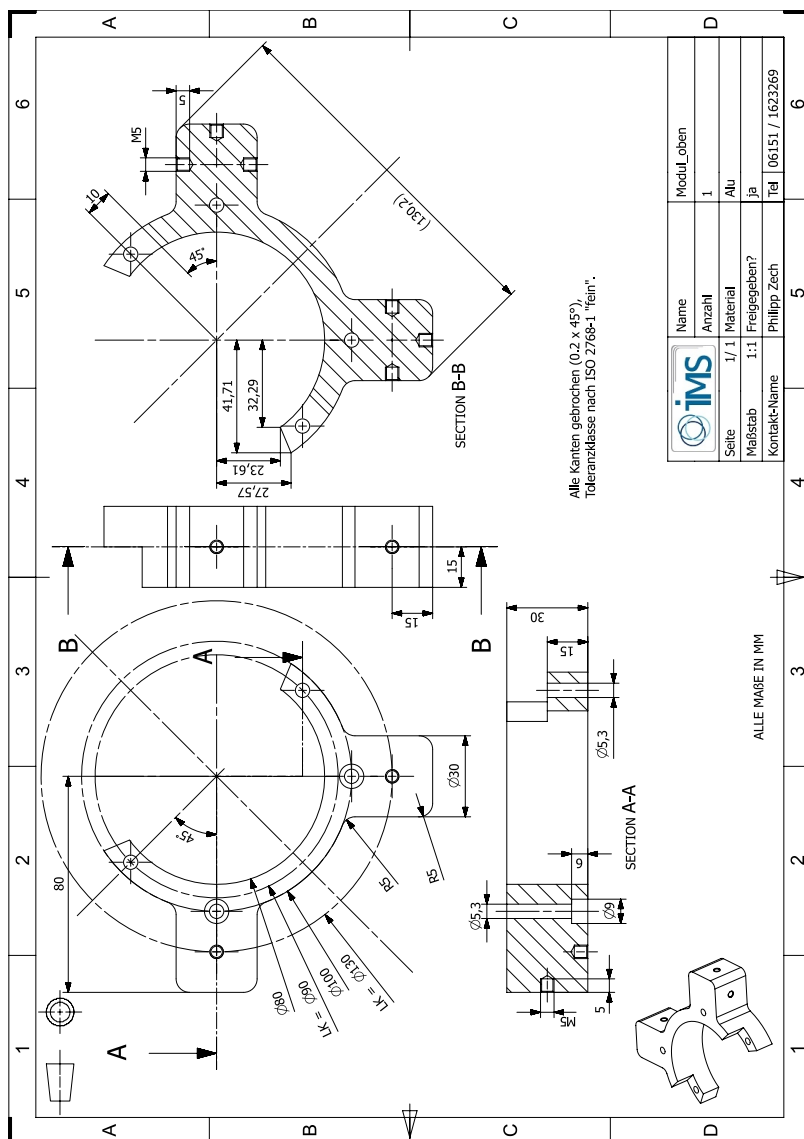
Technische Zeichnung Aktormodul (1/2).
